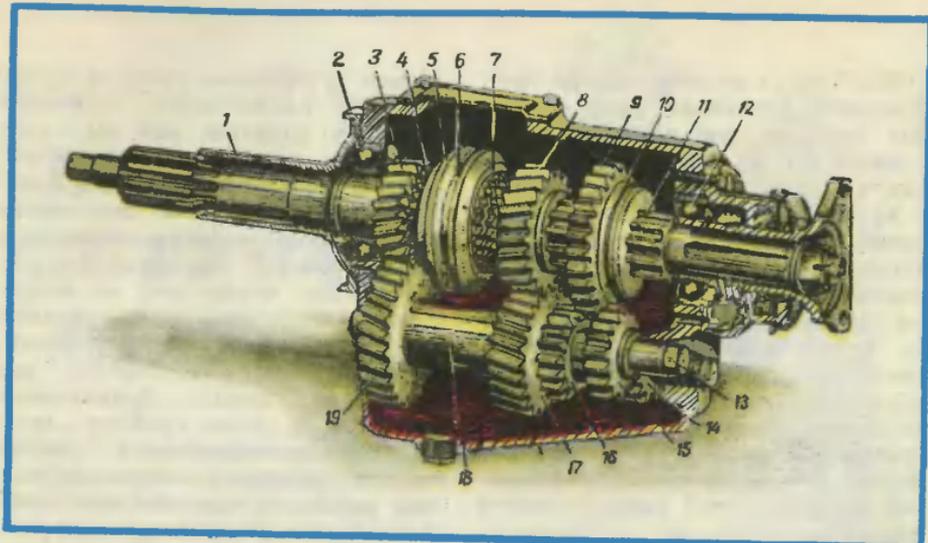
Коробка передач легкового автомобиля: 1 — ведущий вал; 2 — подшипник ведущего вала; 3 — шестерня постоянного зацепления ведущего вала; 4 — зубчатый венец прямой передачи; 5 — муфта синхронизатора; 6 — кольцевая проточка для вилки переключения синхронизатора; 7 — блокирующее кольцо; 8 — шестерня второй передачи ведомого вала; 9 — шестерня-наретка первой передачи и заднего хода; 10 — кольцевая проточка для вилки переключения шестерни-наретки первой передачи и заднего хода; 11 — ведомый вал; 12 — подшипник ведомого вала; 13 — ось промежуточной шестерни заднего хода; 14 — ведущая шестерня заднего хода; 15 — промежуточная шестерня заднего хода; 16 — шестерня первой передачи; 17 — шестерня второй передачи; 18 — промежуточный вал; 19 — шестерня постоянно-
